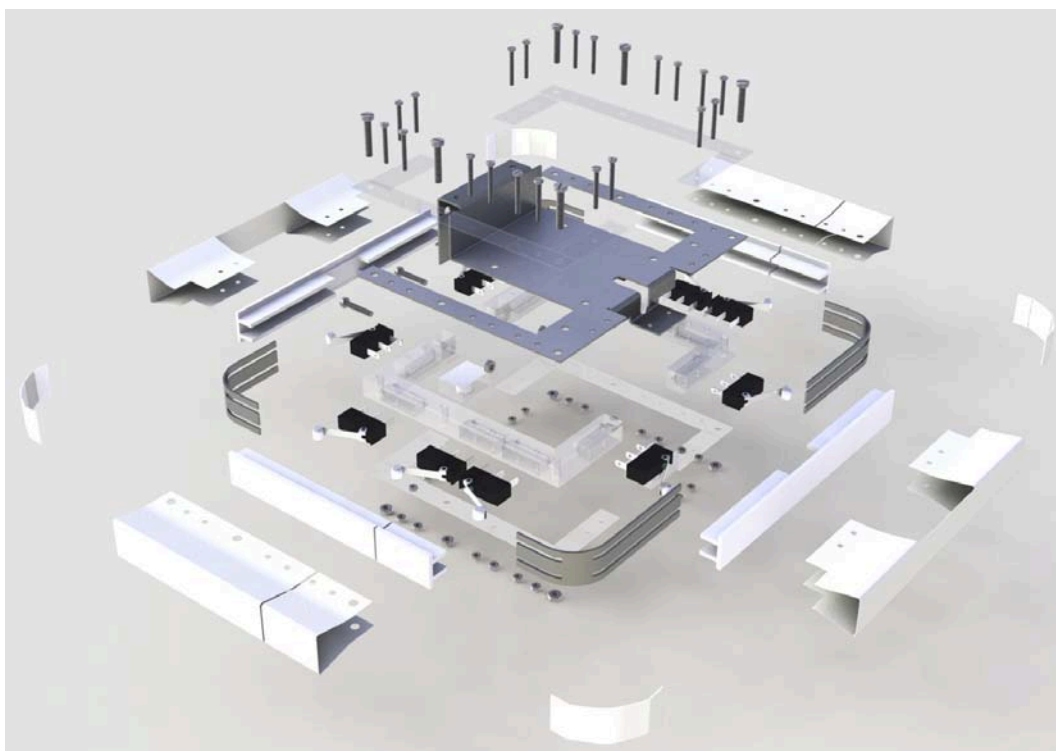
Perspectiva explodida do chassis do SALbot.
